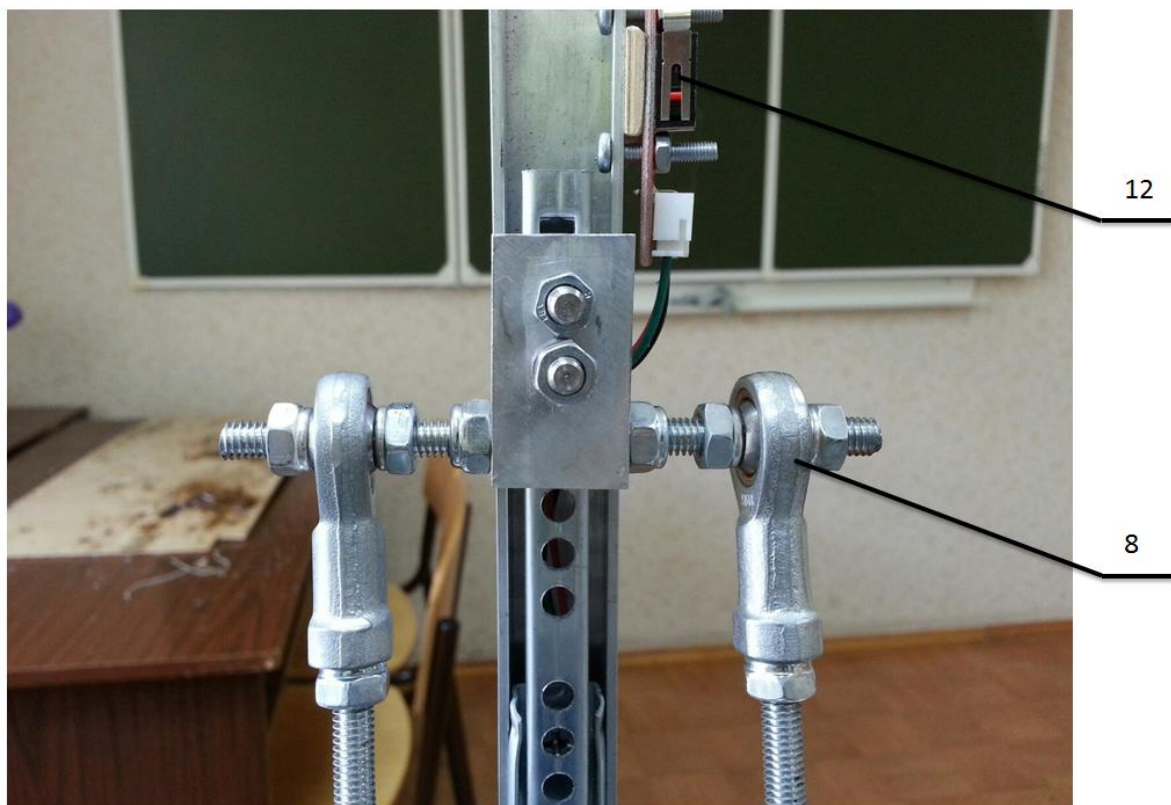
Внешний вид подвижной части станка вверх.
